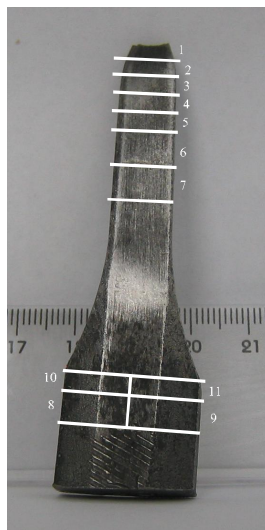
Разрушившийся при продольном растяжении образец стали 35Г2С со схемой нарезки образцов для испытаний. Верхняя часть - зона разрушения, нижняя часть зона закрепления образца в разрывной машине.
